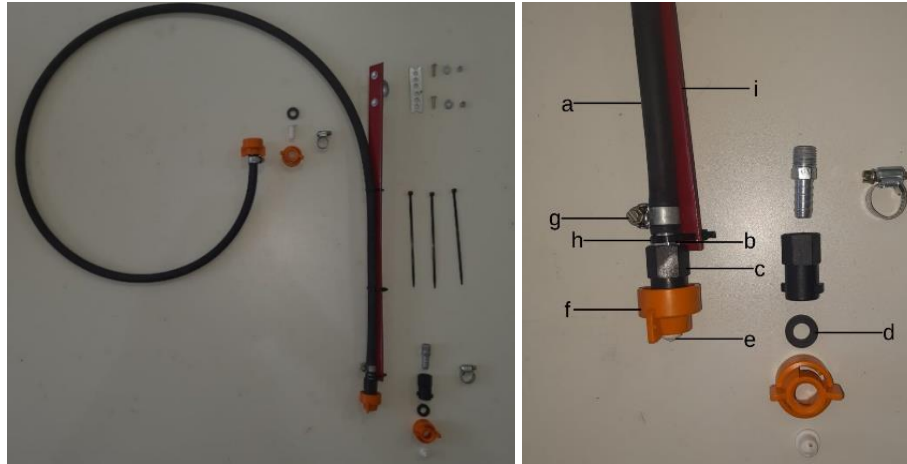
Montagem dos pingentes A. Componentes necessários para a montagem. B. Detalhe da montagem.
